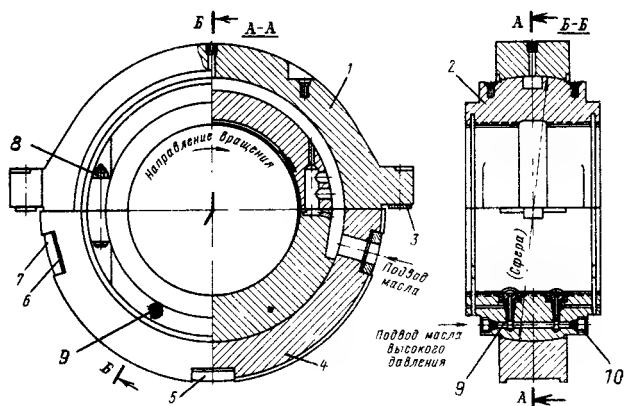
Опорный подшипник турбины К-500-65/3000:
